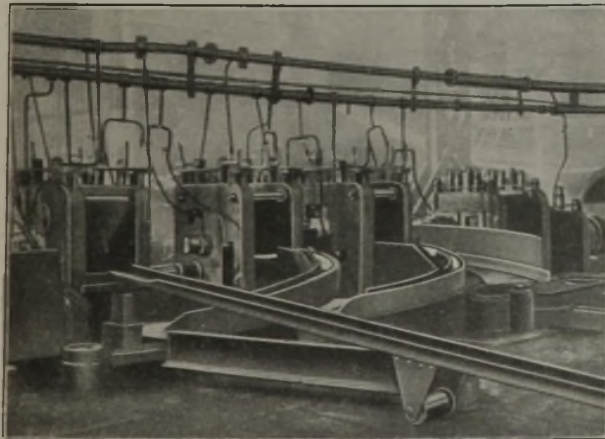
Rund-Umführungen vor dem 1., 2. und 3. Walzgerüst.
